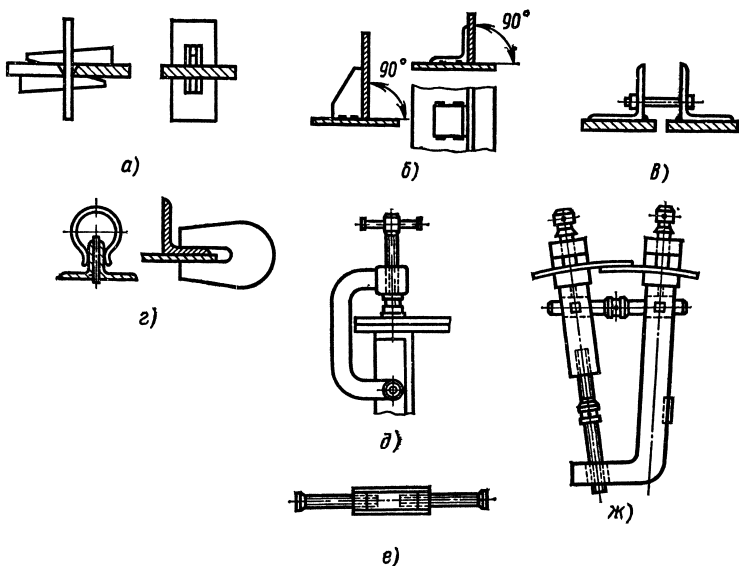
Универсальные сборочные приспособления для сварки:
